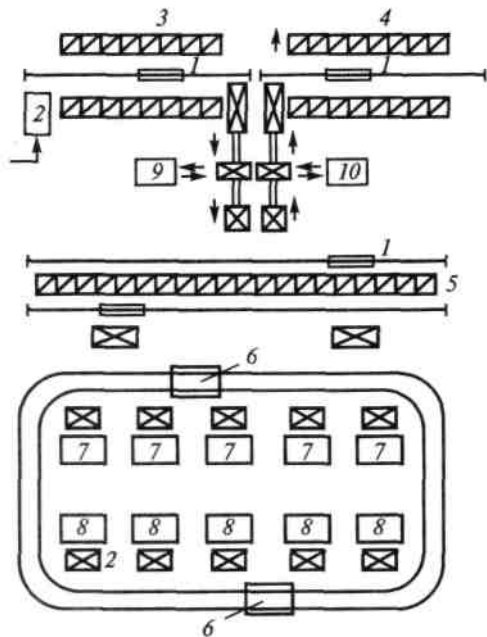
Компоновка гнучкої системи для обробки корпусних деталей (дрібносерійне виробництво):
